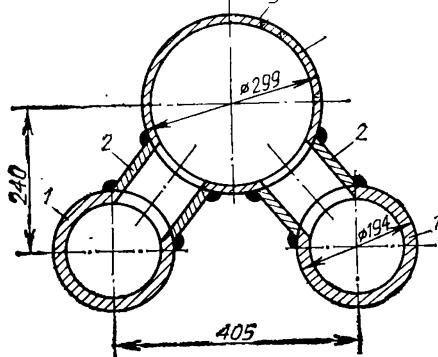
Поперечное сечение водоохлаждаемой балки:
